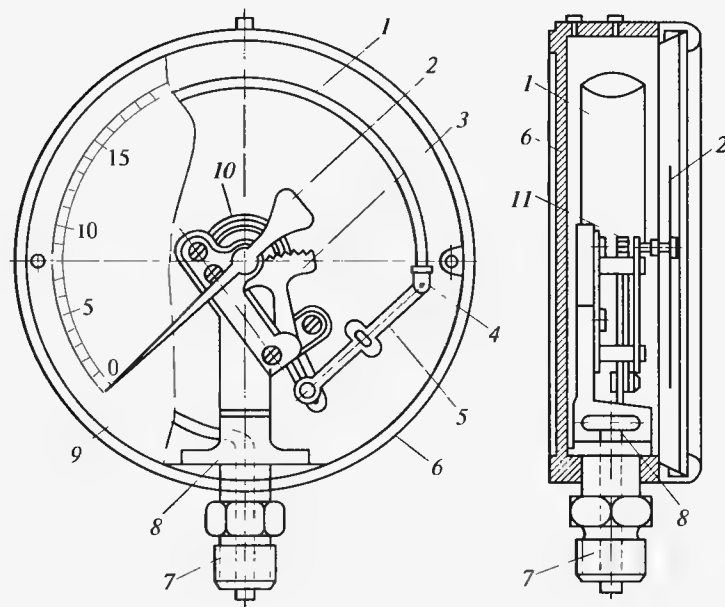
Показывающий манометр с одновитковой трубчатой пружиной: 1 — трубчатая пружина; 2 — стрелка; 3 — зубчатый сектор; 4 — пробка; 5 — поводок; 6 — корпус; 7 — штуцер; 8 — держатель; 9 — шкала; 10 — спиральная пружина; 11 — шестеренка
